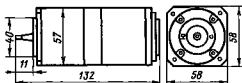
22 Габаритные и установочные размеры двигатель-генератора ИЭ-10
